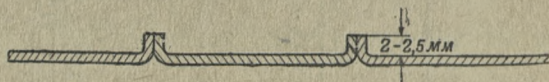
Отбортовка края пробоины и лючка перед заваркой
